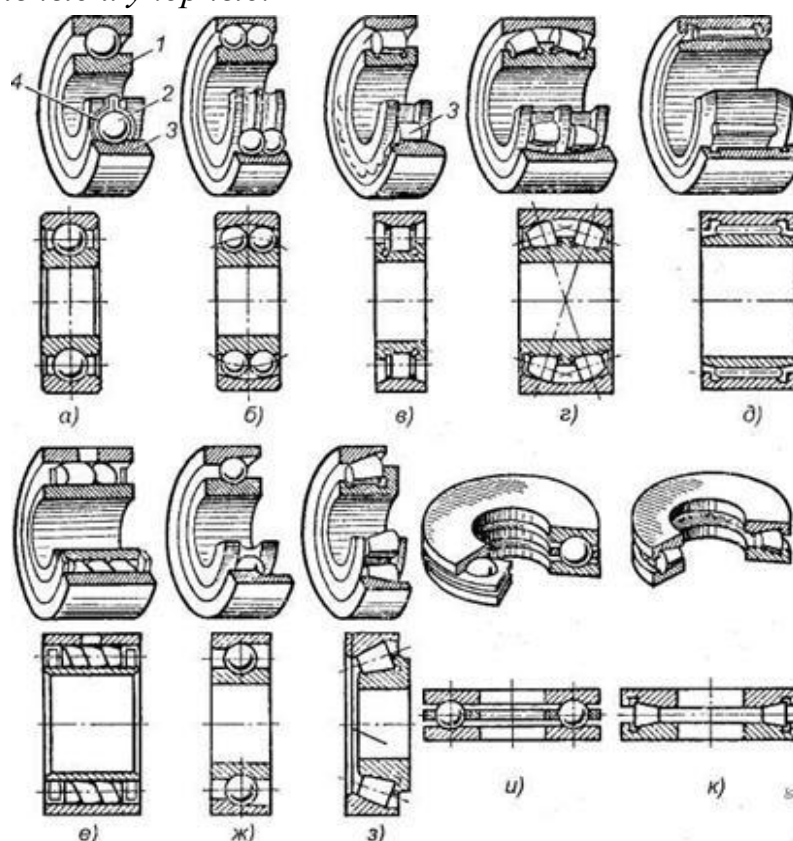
Подшипники качения: а, б, в, г, д, е — радиальные подшипники; ж, з — радиально-упорные подшипники; и, к — упорные подшипники; 1 — внутреннее кольцо; 2 — тело качения; 3 — наружное кольцо; 4 — сепаратор.
